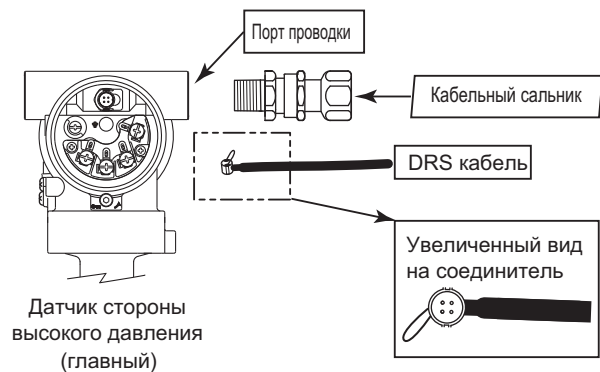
Монтаж с использованием кабельного сальника для кабеля DRS
